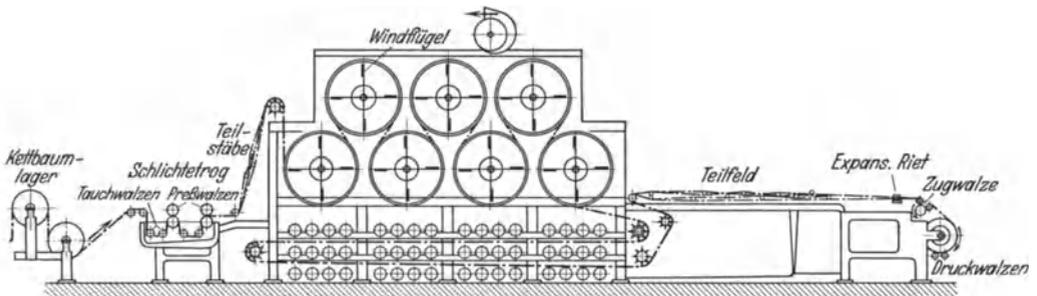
Kettenführung durch eine Lufttrocken-Schlichtmaschine.
